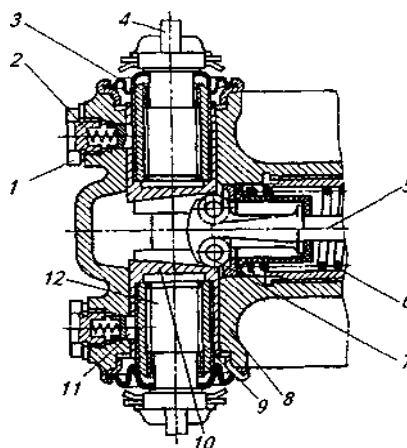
Клиновое разжимное устройство автомобиля КАЗ-4540 с автоматической регулировкой зазора: 1 — пробка; 2 — пружина; 3 — грязезащитный колпак; 4 — тормозная колодка; 5 — клин; 6 — пружина; 7 — ролик; 8 — суппорт; 9 — регулировочная втулка; 10 — толкатель; 11 — штифт-храповик; 12 — регулировочный винт
